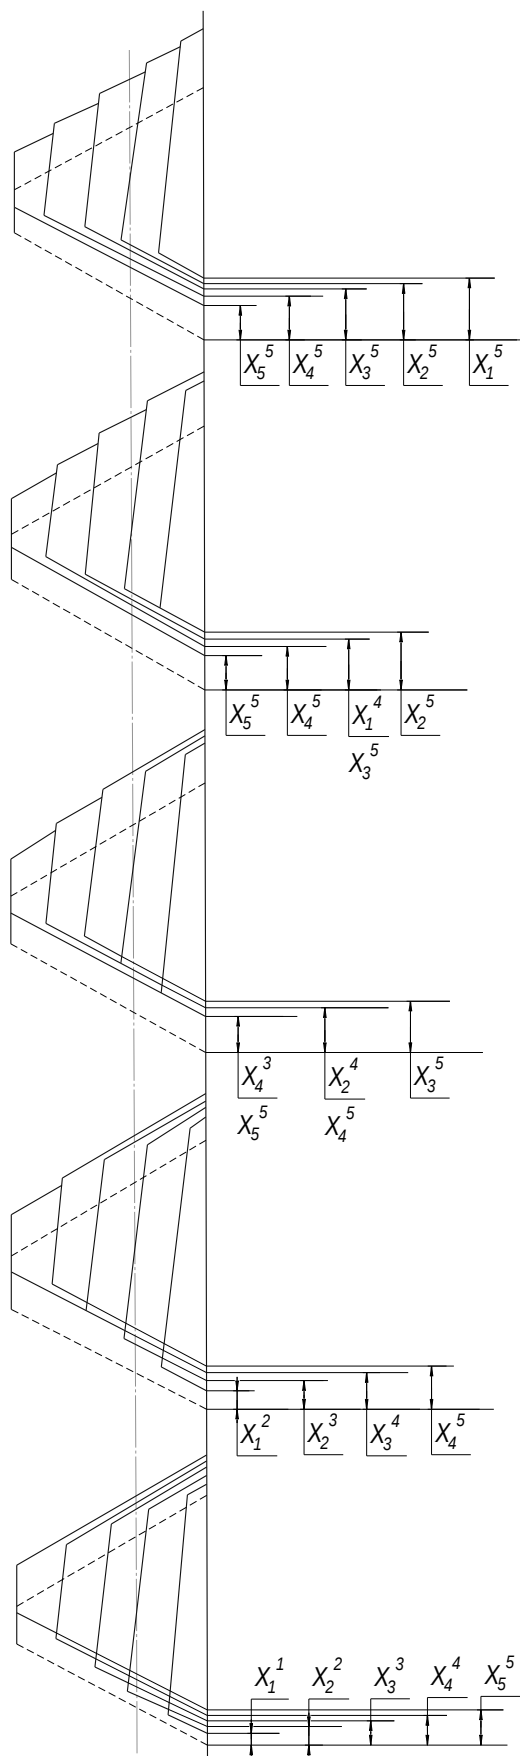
Схема искажений профиля образуемой резьбы за счет деформации кручения рабочей части режущего метчика
